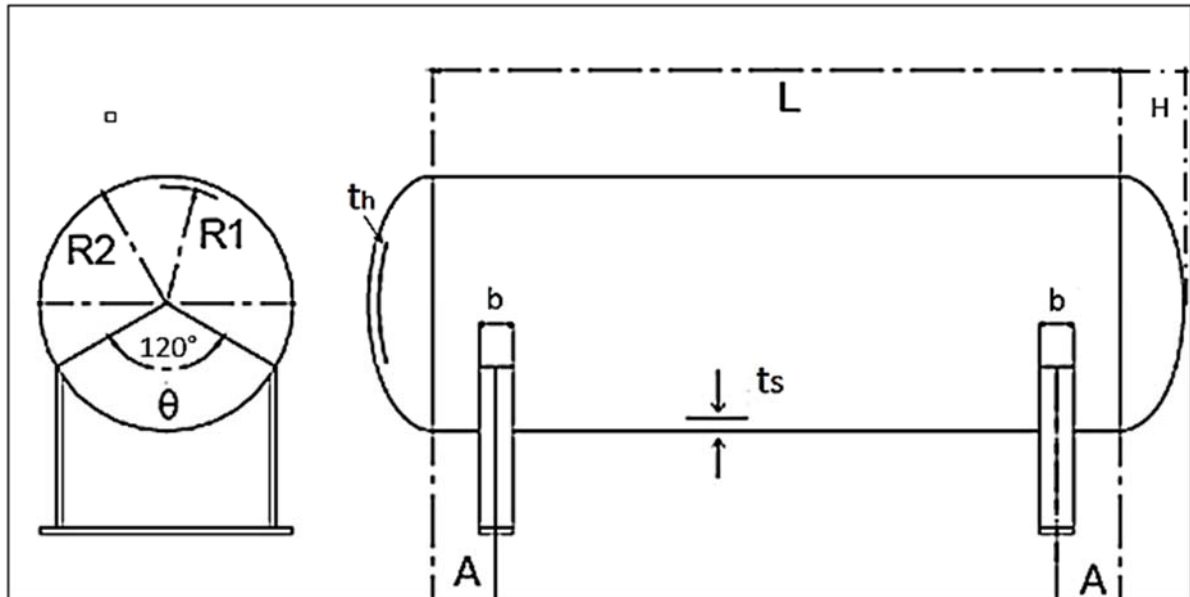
Dimensiones del tanque sometido a presión interna.
